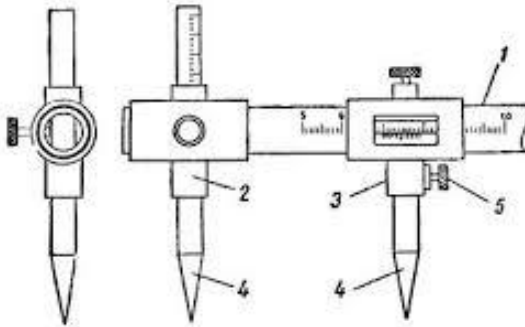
Розмічувальний штангенциркуль: 1 – лінійка; 2 – нерухома ніжка; 3 – рухома ніжка; 4 – голки; 5 – гвинт
